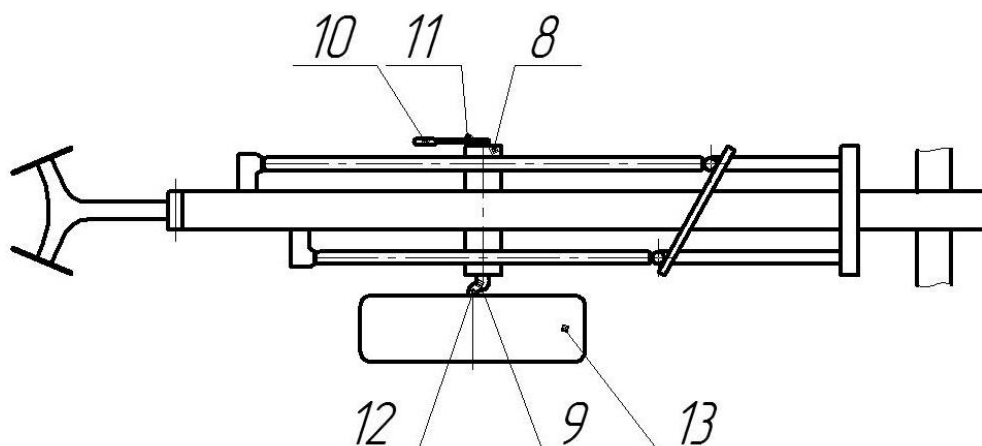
Конструкторско-технологическая схема сошника зернотуковой сеялки (вид сверху)
